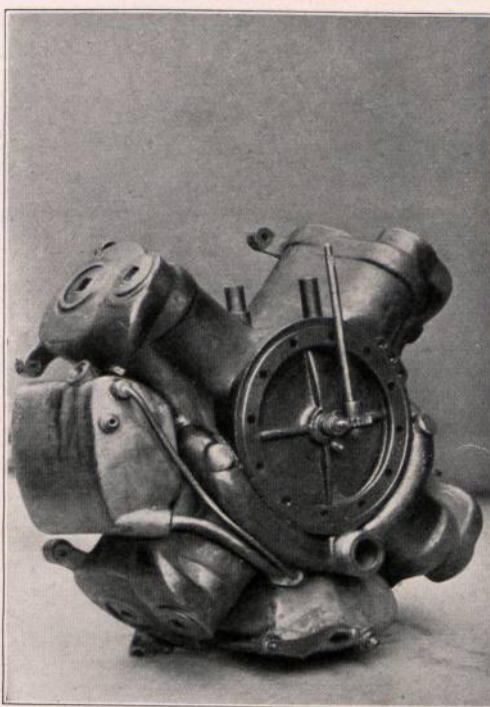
Vierzylinder-Maschine mit Ölgefäßen.
